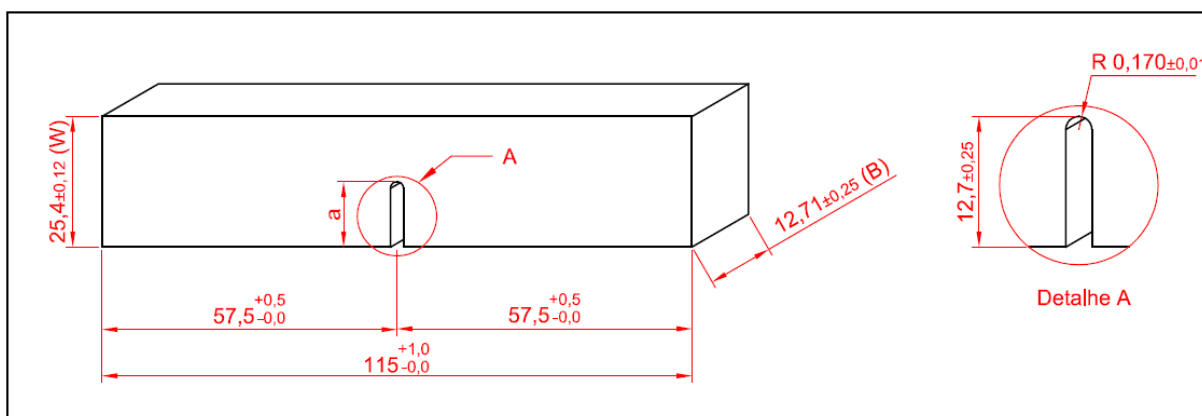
Desenho de fabricação do CP de flexão, formato SE(B), com entalhe em “U”.
